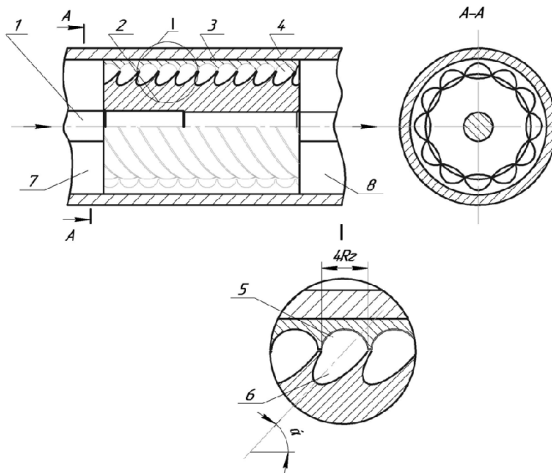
Удосконалені робочі органи насоса [8]: 1 – привідний вал; 2 – гвинт; 3 – втулка; 4 – корпус; 5 – гвинтова канавка напівкруглої форми; 6 – гвинтова канавка двогастої форми; 7 – камера підводу; 8 – камера відводу.
